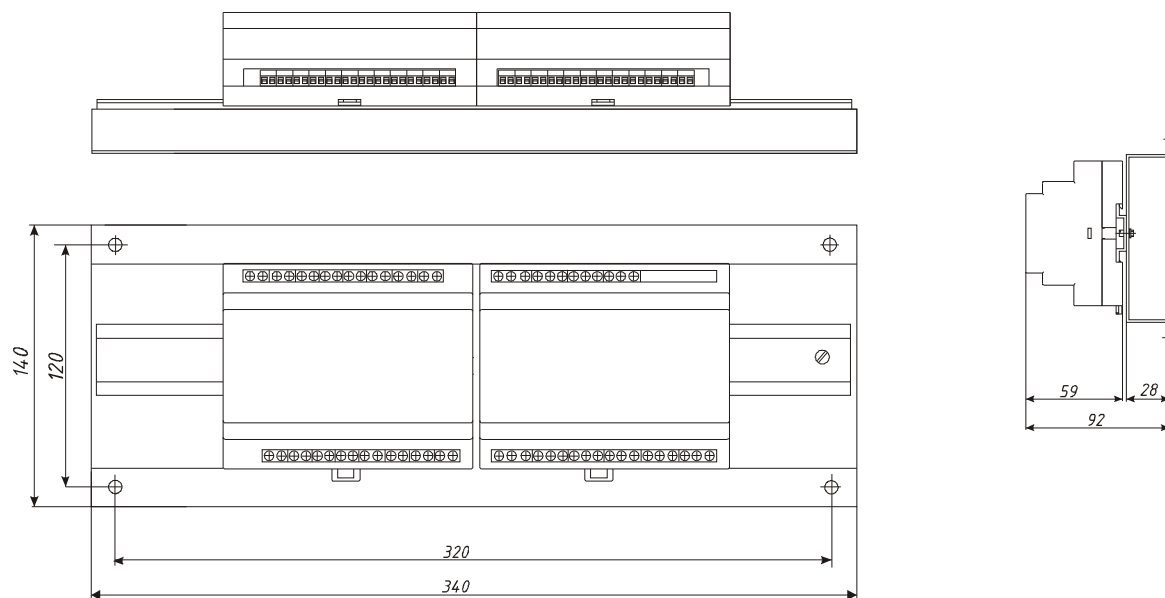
Габаритные размеры основного блока прибора Мерадат-М25Е6/...../
